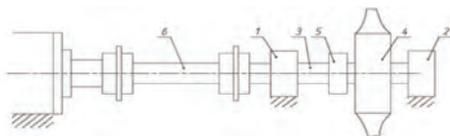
Компоновка ротора: 1 – радиальная подшипниковая опора; 2 – радиально-упорная подшипниковая опора; 3 – коренной вал ротора; 4 – РК; 5 – исполнительный механизм поворота лопаток РК; 6 – трансмиссионный вал
